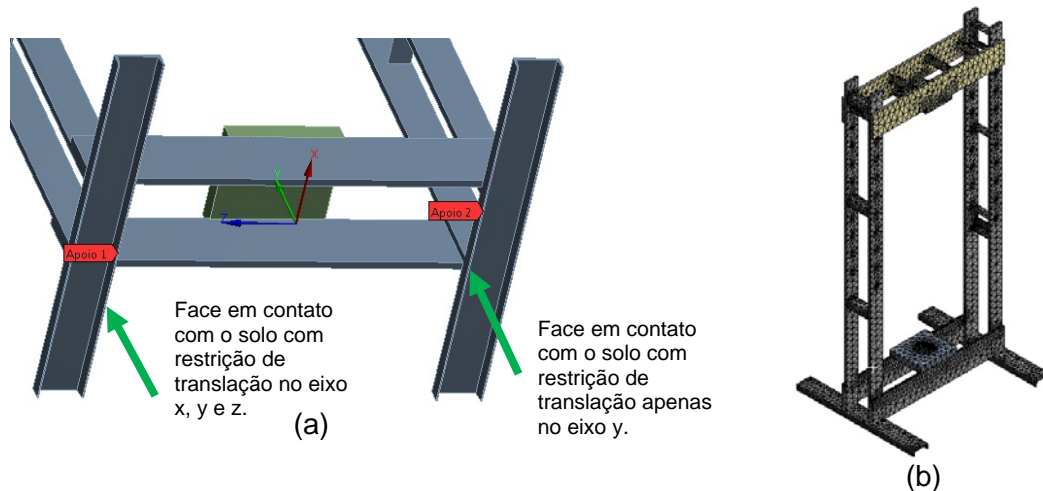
Restrições de movimento aplicadas ao modelo (a); e malha de elementos finitos planos (b).
